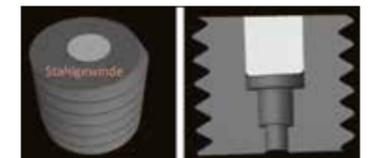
Pyrotechnischer Initiator: 3D-Rekonstruktion eines in einer Stahlschraube enthaltenen Bauteils (links). Der 2D-Schnitt zeigt ein Detail der inneren Baugruppe (rechts)
